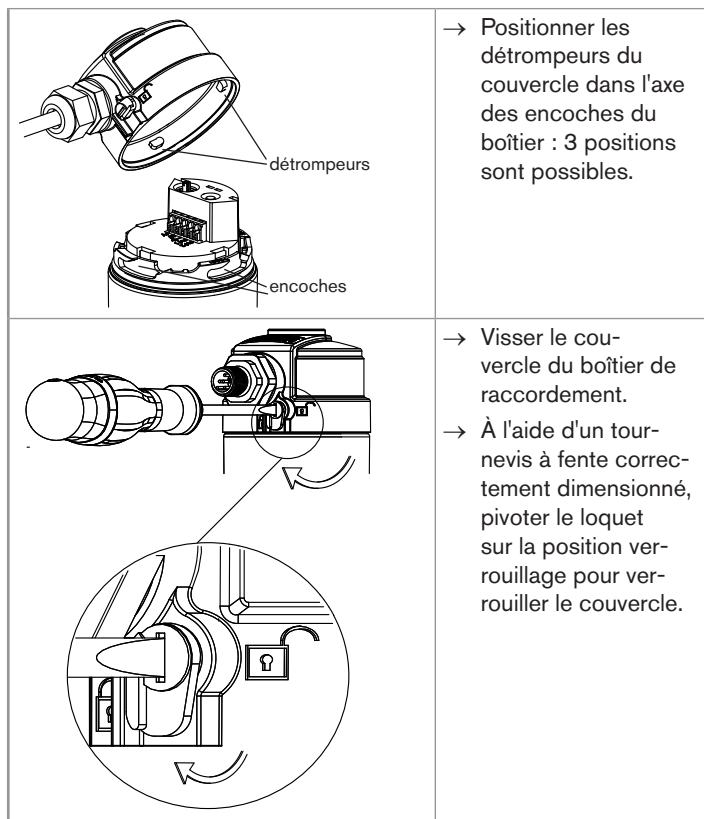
Mise en place du couvercle du boîtier de raccordement
